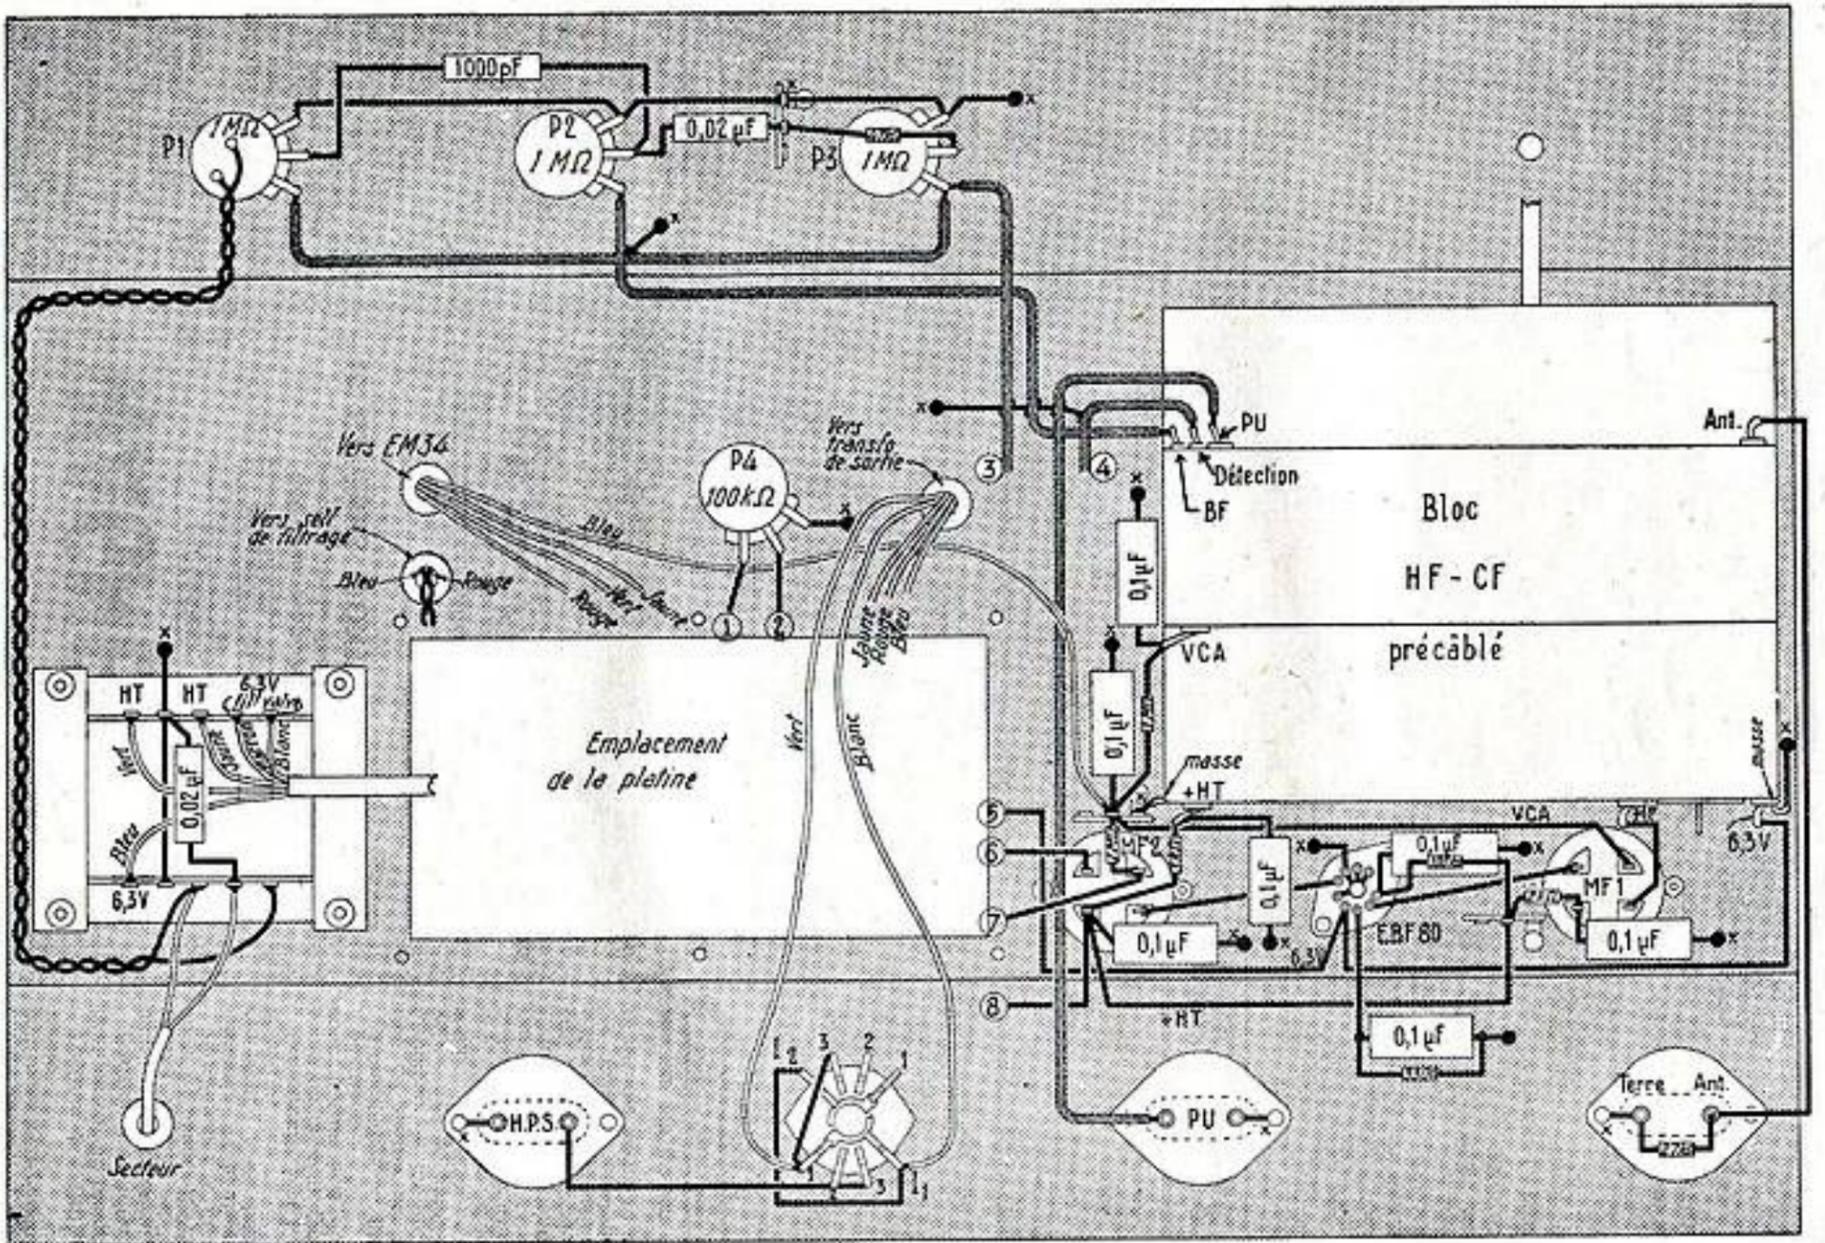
Plan de câblage de la platine pouvant être fournie pré câblée
